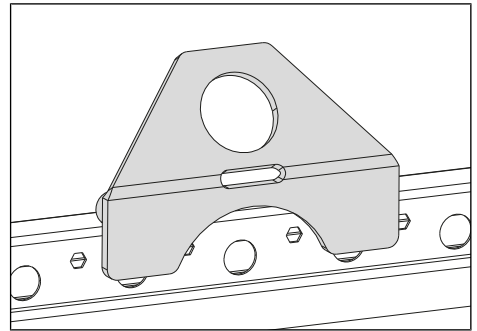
Adaptor de lanț Multi Flex la cadrul exterior Multi Lock
